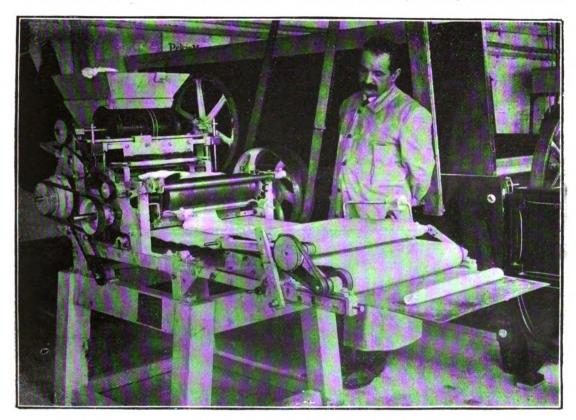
MACHINE A FABRIQUER LES PAINS.
